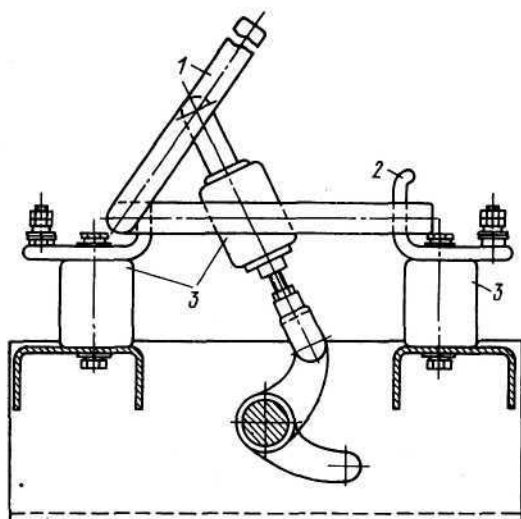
Элемент разъединителя механической блокировки на опорных изоляторах
